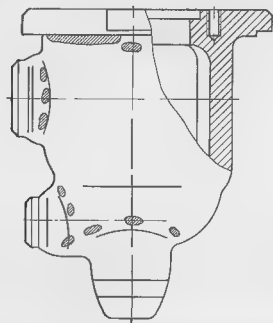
Места появления трещин в корпусе стопорного клапана
